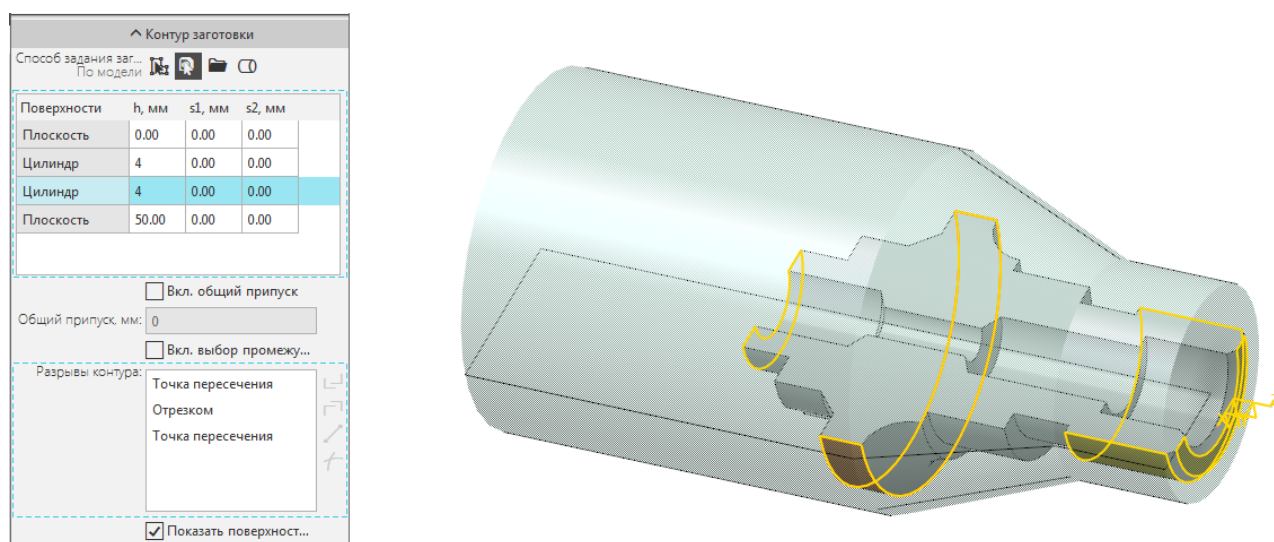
Заготовка, созданная относительно поверхностей детали
